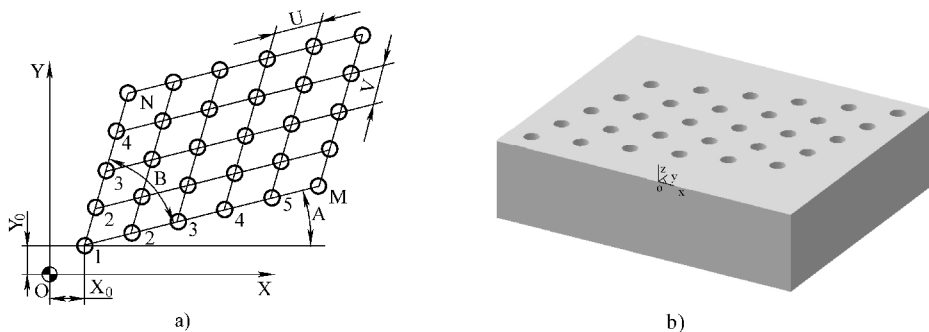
平行四边形网式点阵孔群类零件钻削加工刀具路线示意图
